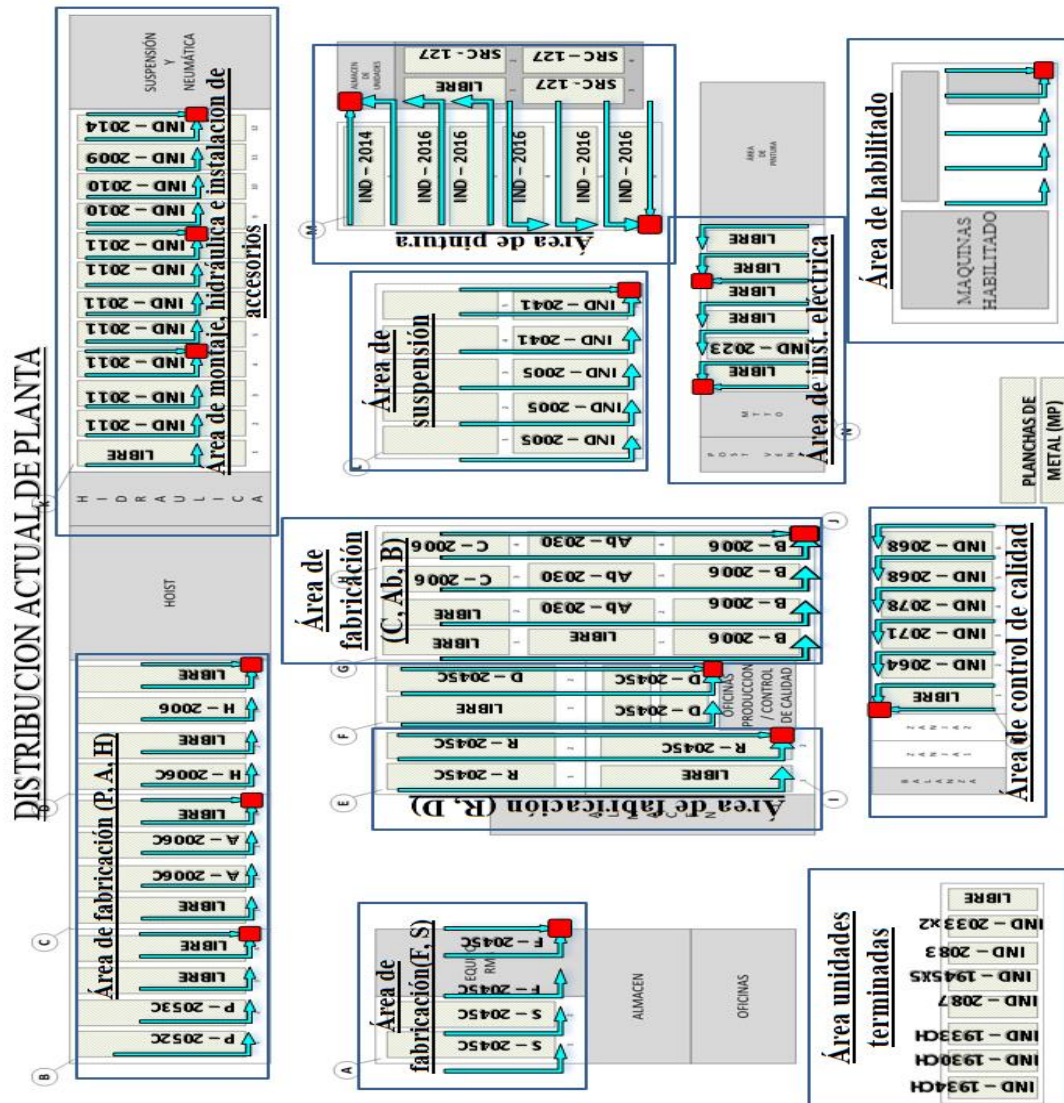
Trayecto de limpieza en las áreas de trabajo de la planta.
